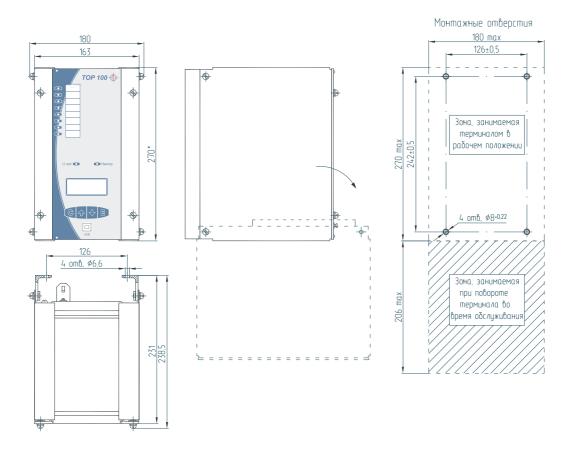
Габаритные и установочные размеры для навесного монтажа
